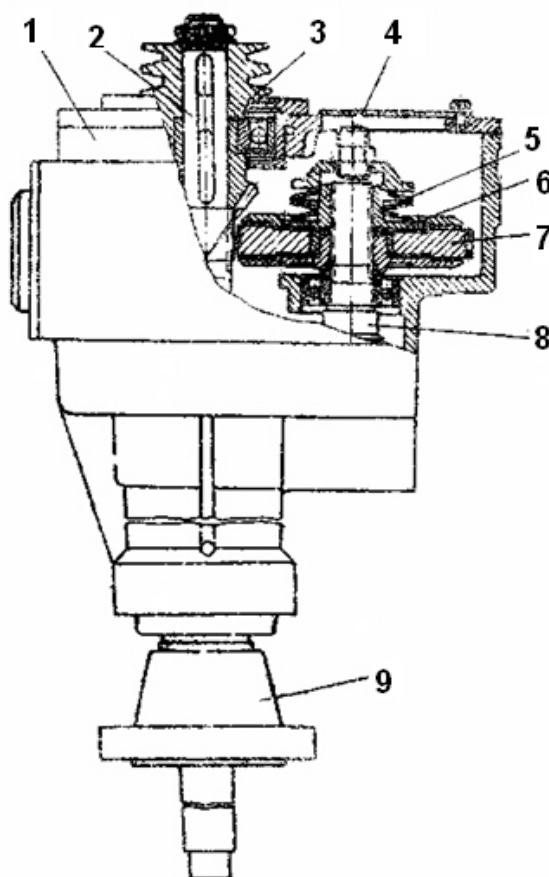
Регулировка фрикционной муфты конического редуктора:
